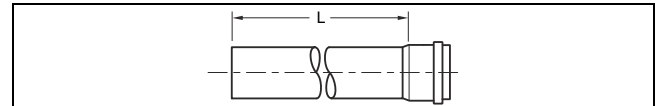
Дымовой трубы \varnothing 80/ \varnothing 110
